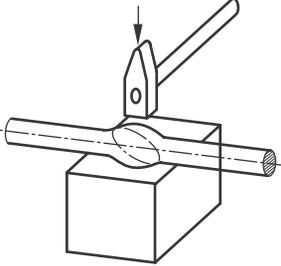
Wirkpaarungen beim Schweißen
